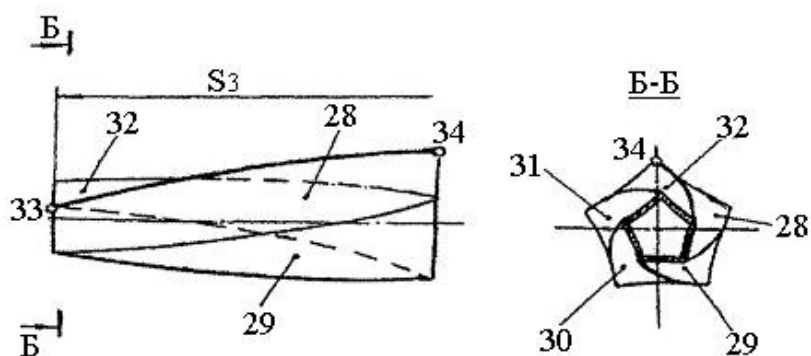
Часть корпуса вращающейся печи для приготовления цементного клинкера с пятью винтовыми ребрами (28,29,30,31,32- трапециевидные листы, 33-34- одно из пяти винтовых ребер)
